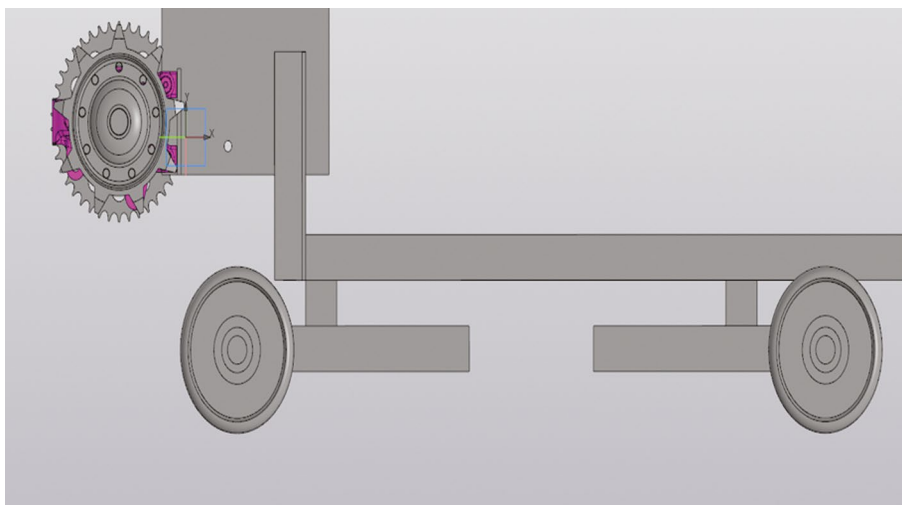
Гусеница с ведомой звездочкой и опорными катками
